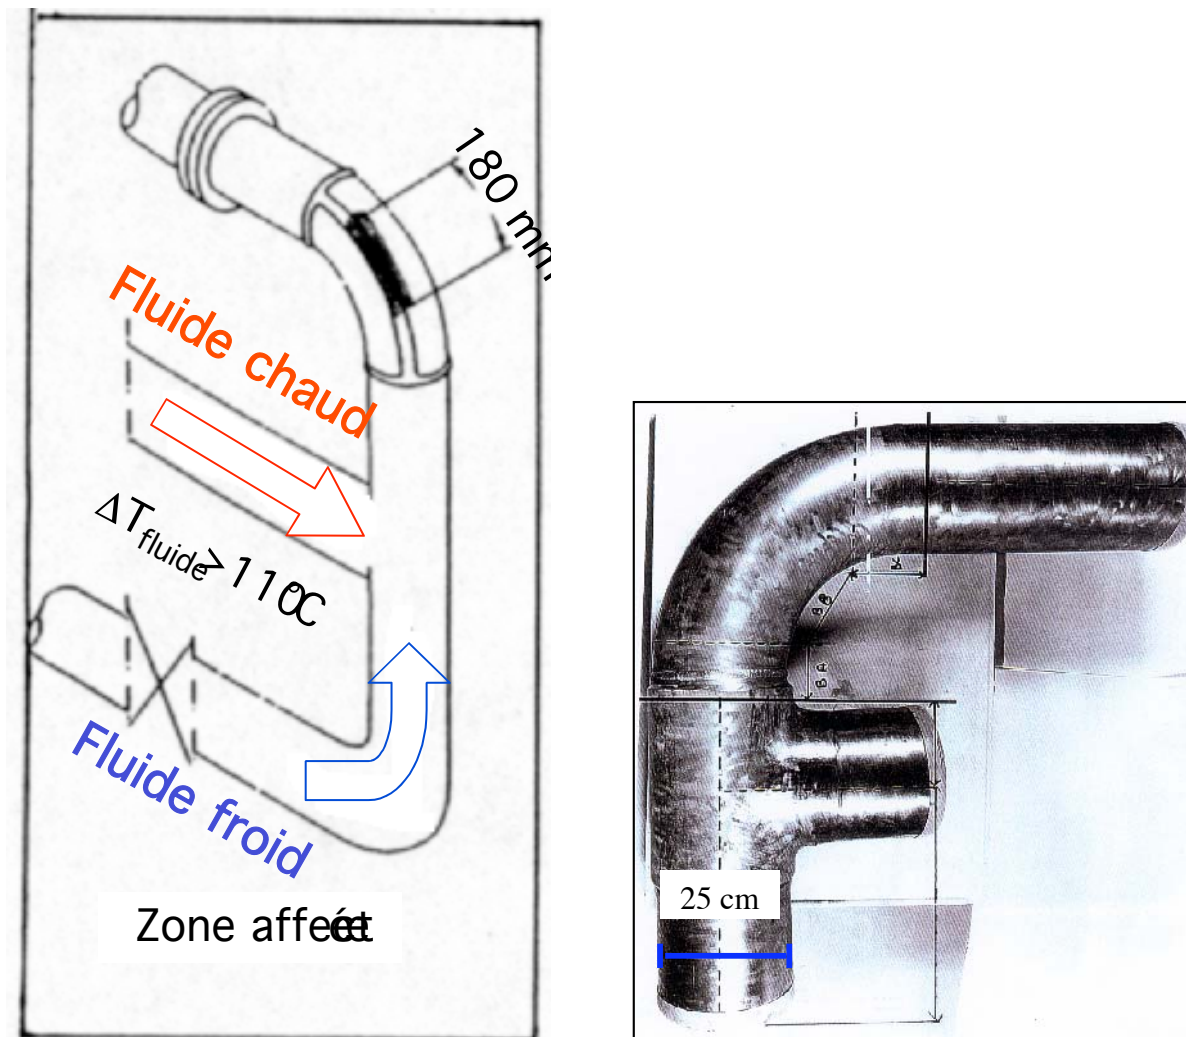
Schéma du coude sur lequel la fissure traversante est apparue le long de la soudure longitudinale extrado (circuit RRA) (Faidy C. 2002).
